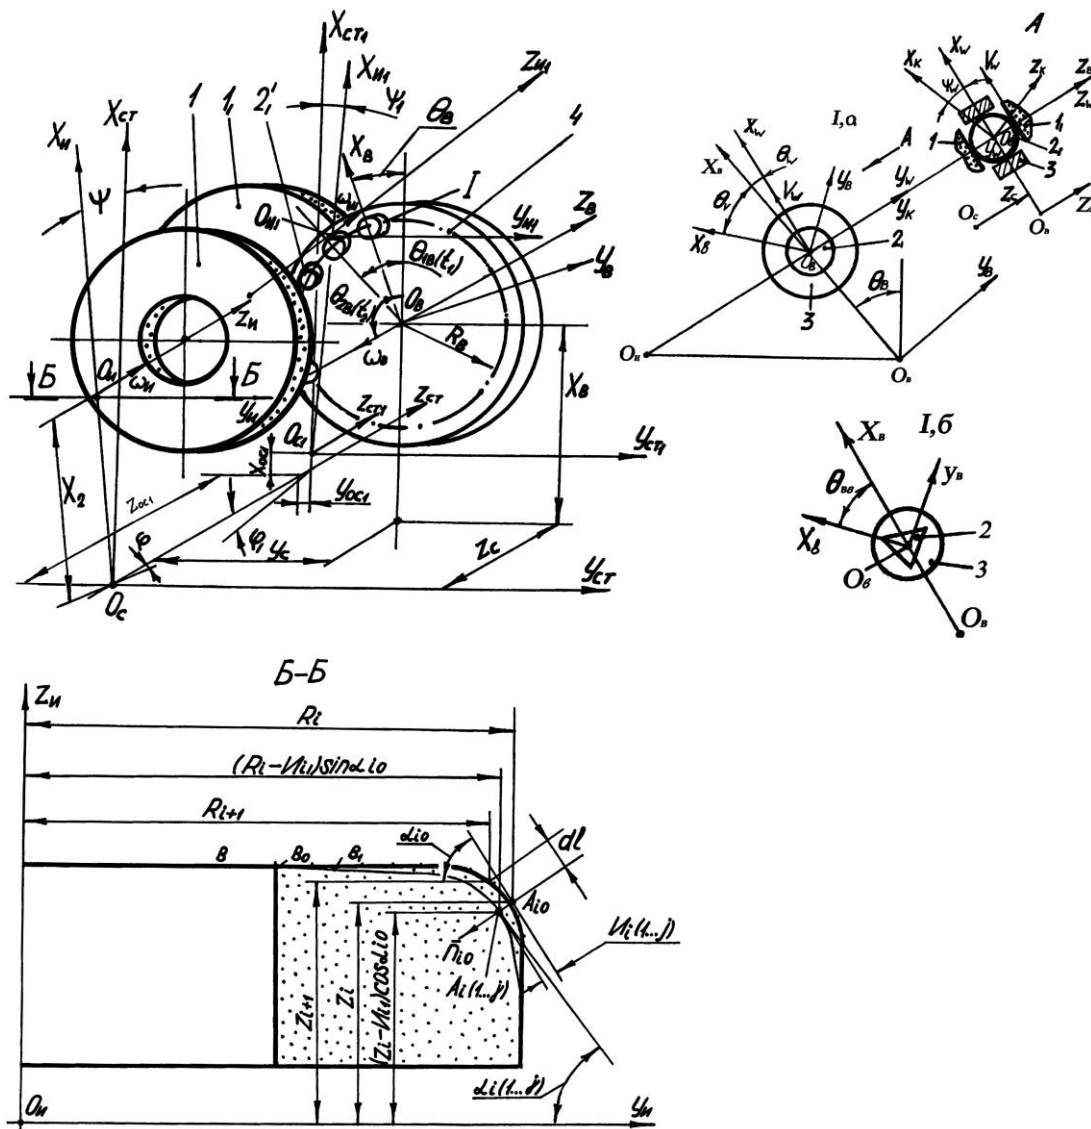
Общая схема формообразующих систем станков для шлифования различных поверхностей со скрещивающимися осями кругов и деталей
